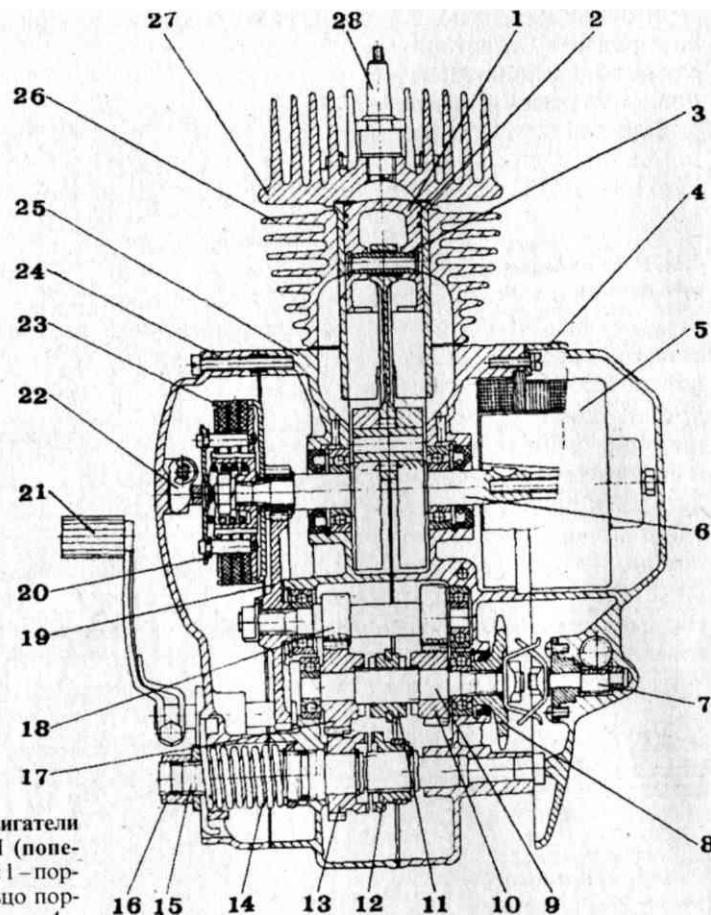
Двигатели B50M, B501M (поперечный разрез): 1 - поршень; 2 - кольцо пор-
